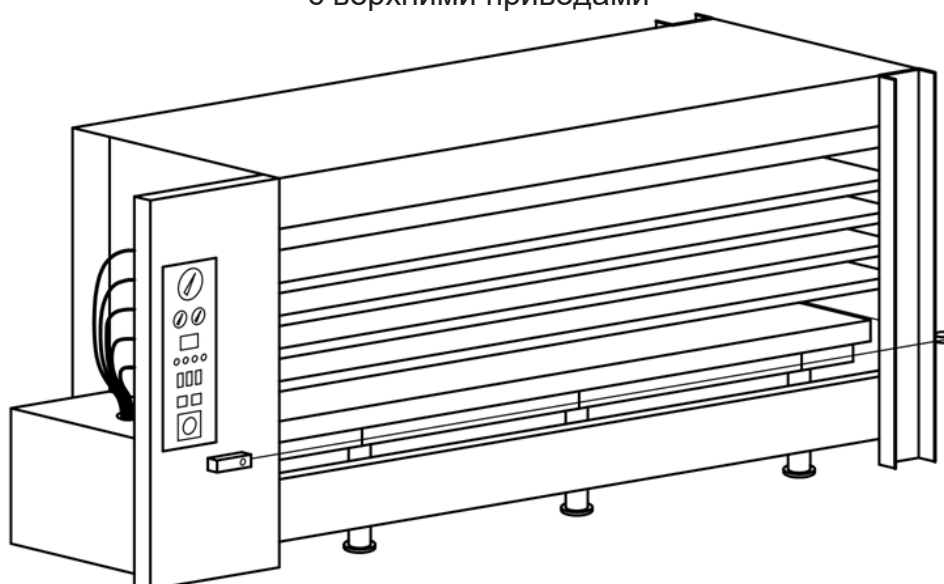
Пример прессы горячего прессования с промежуточными плитами
